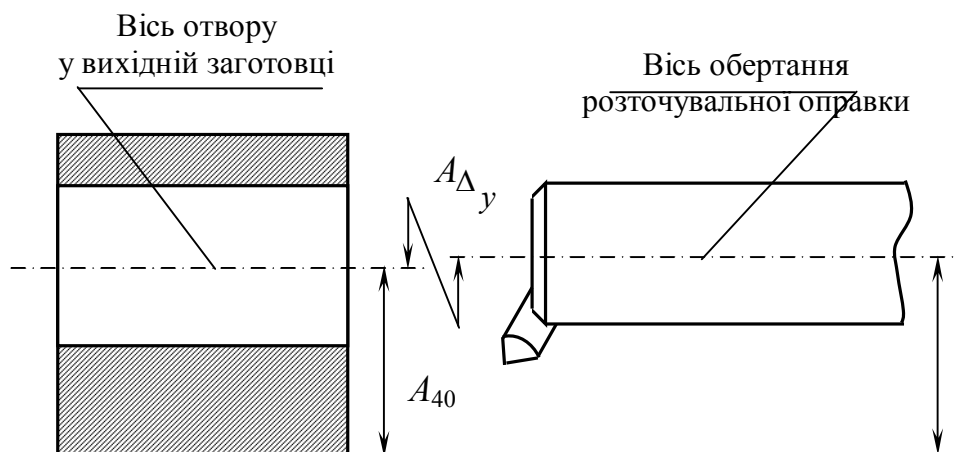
Схема розмірного ланцюга для визначення похибки базування у напрямі осі Y
